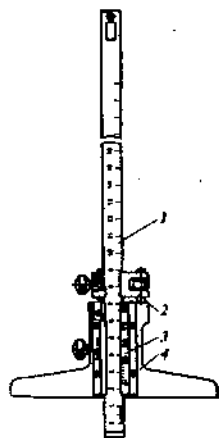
Штангенглубиномер: 1 – штанга-линейка; 2 – рамка микрометрической подачи; 3 – нониус; 4 – основание
